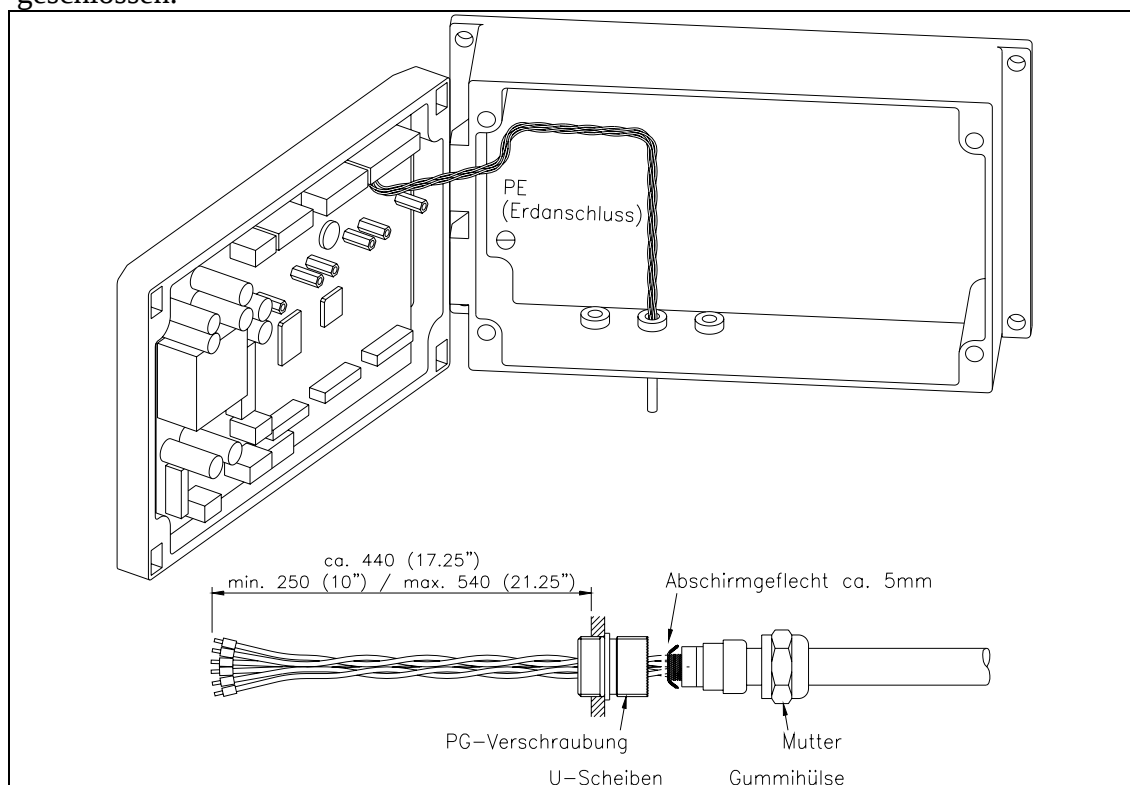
Verlauf der Anschlusskabel im Gehäuse
